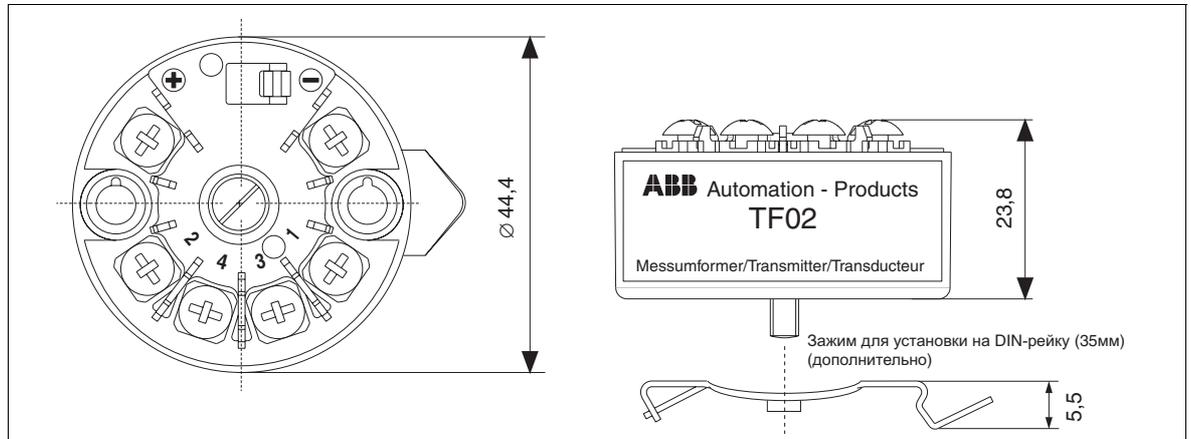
Габаритный чертеж TF02 / TF02-Ex (все размеры в мм)
